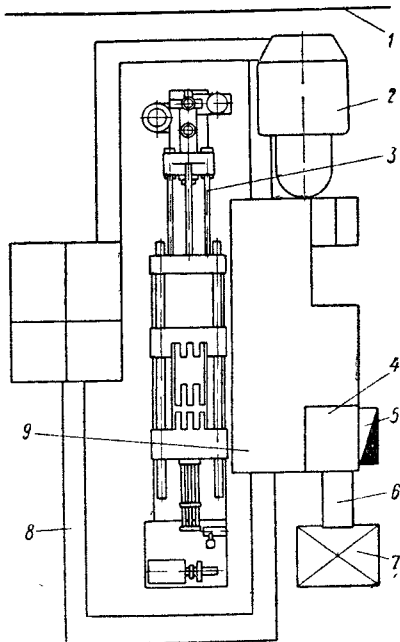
Расстановка комплекса оборудования для литья под давлением и обрубки:
